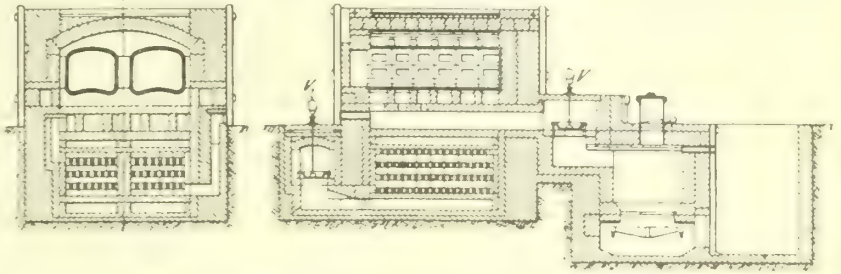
Zwillingsmuffelofen mit Gaserzeuger und Regenerator.
